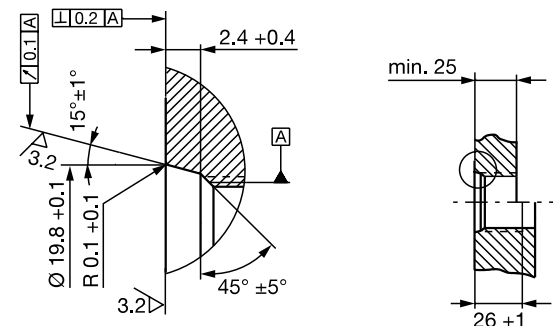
Einschraubloch M18x1.5 nach ISO 6149 O-Ring 15.4x2.1
